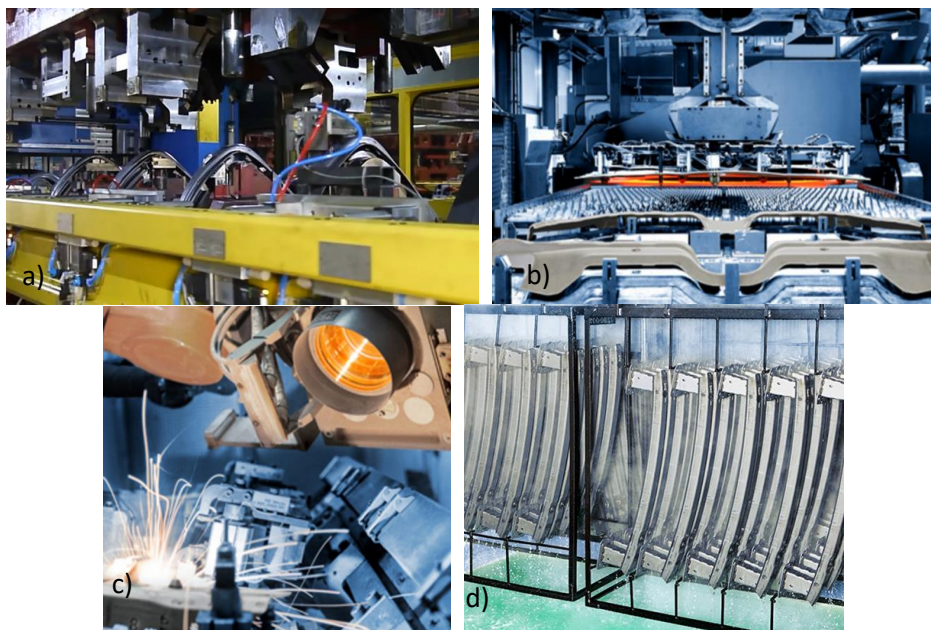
a) Estampagem a frio; b) Estampagem a quente; c) Soldadura; d) Pintura catódica por imersão [75]
